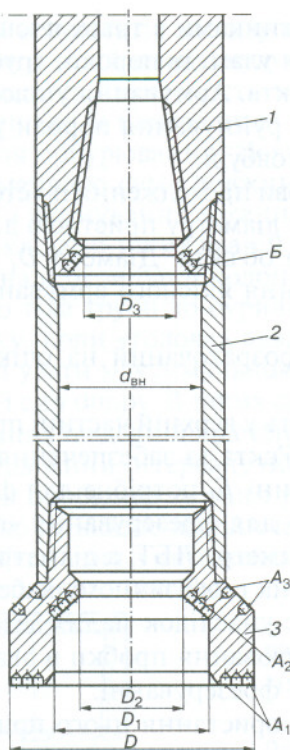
Схема пристрою для обдирювання, обробки верхньої частини аварійного об'єкта і з'єднання з ним ловильного інструменту:
